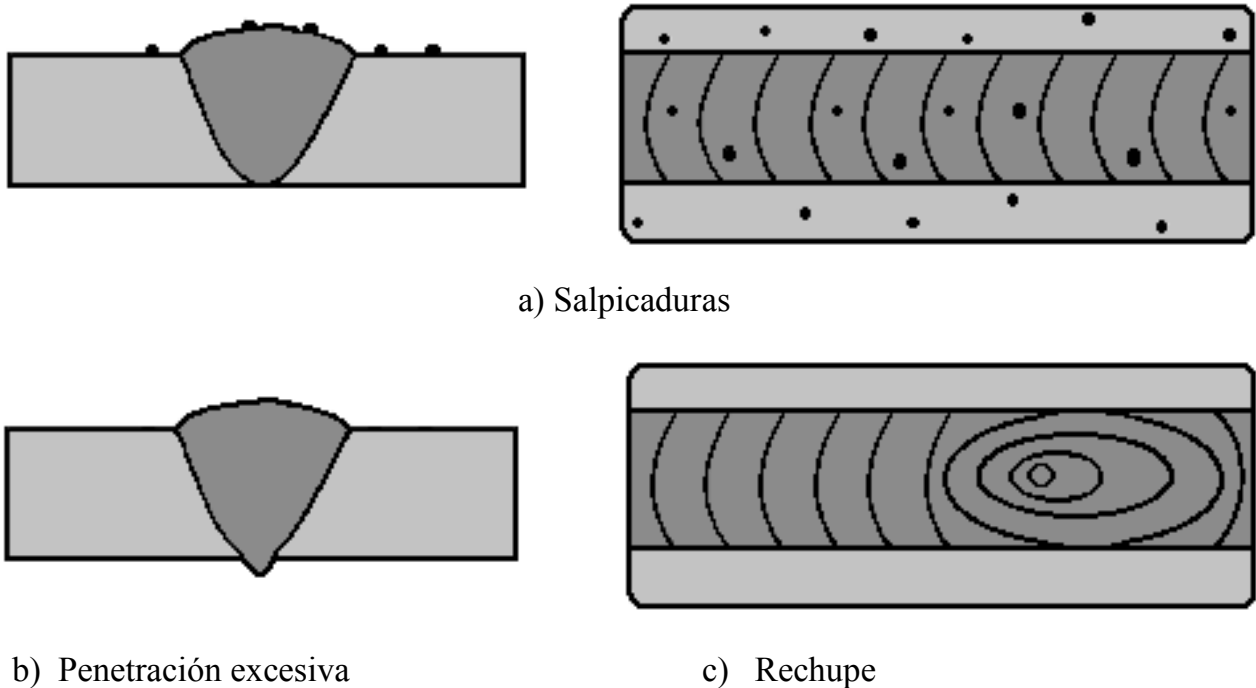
Algunos tipos de defectos en la soldadura (8, 18)
